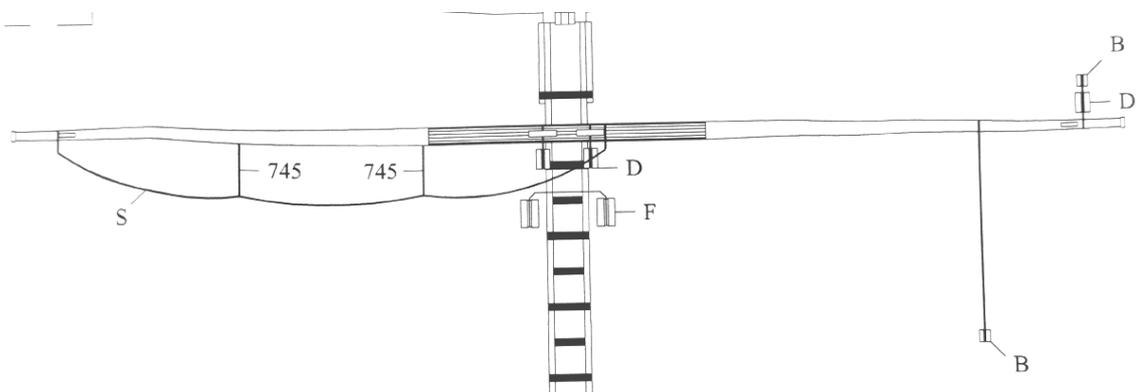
Besanrah mit Blöcke - Planblatt 8
